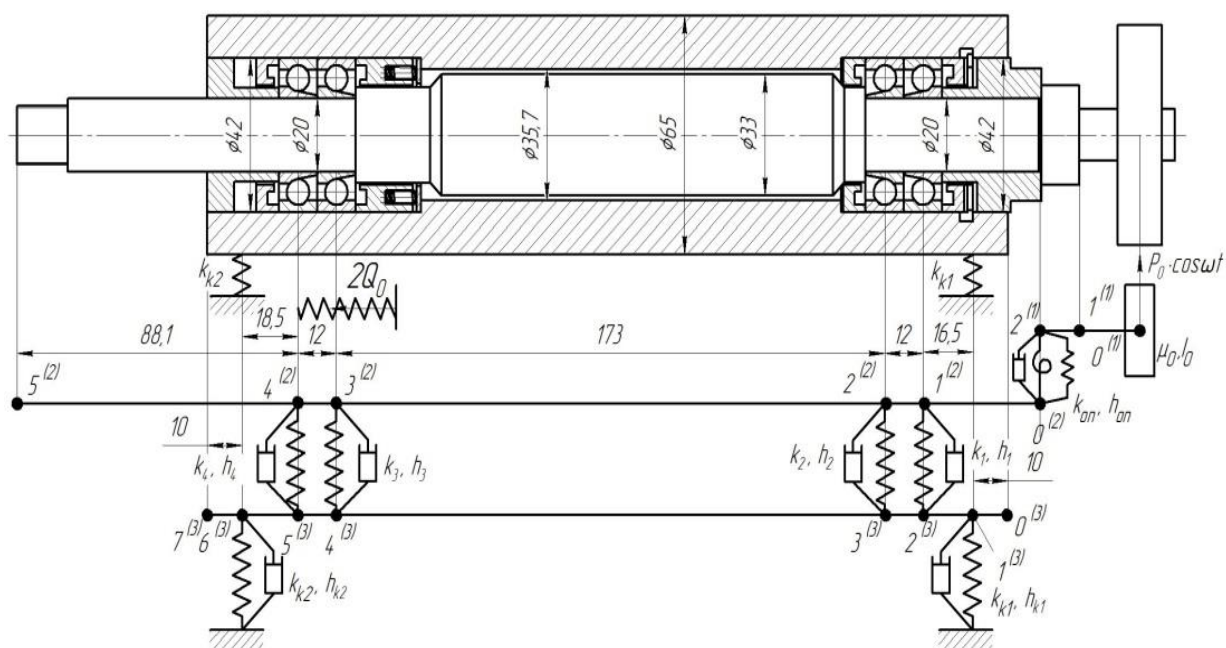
Конструктивна і розрахункова схеми системи «шпиндельний вузол»
